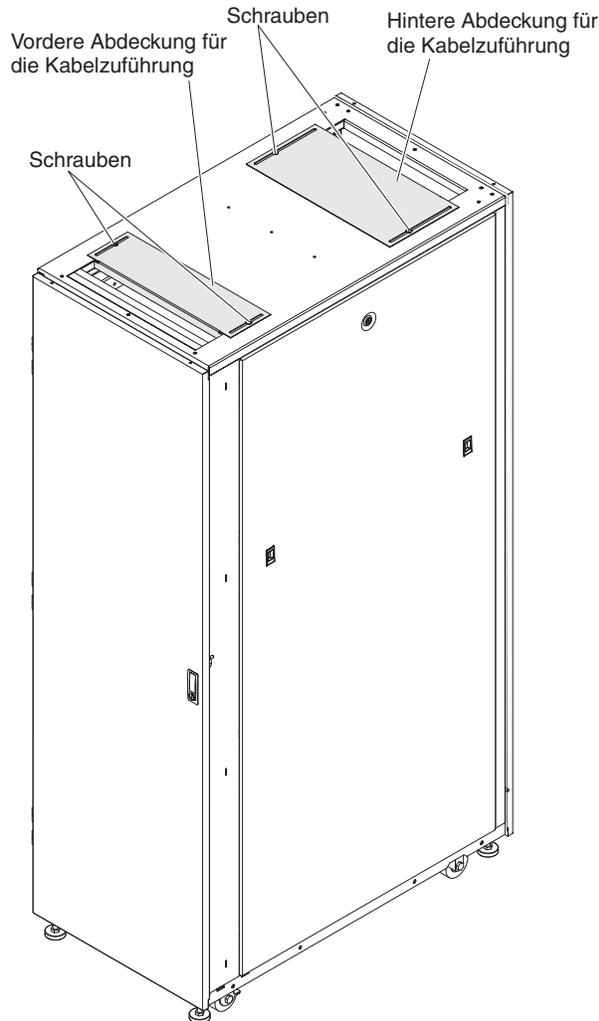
Position der Öffnungen für die Kabelzuführung
